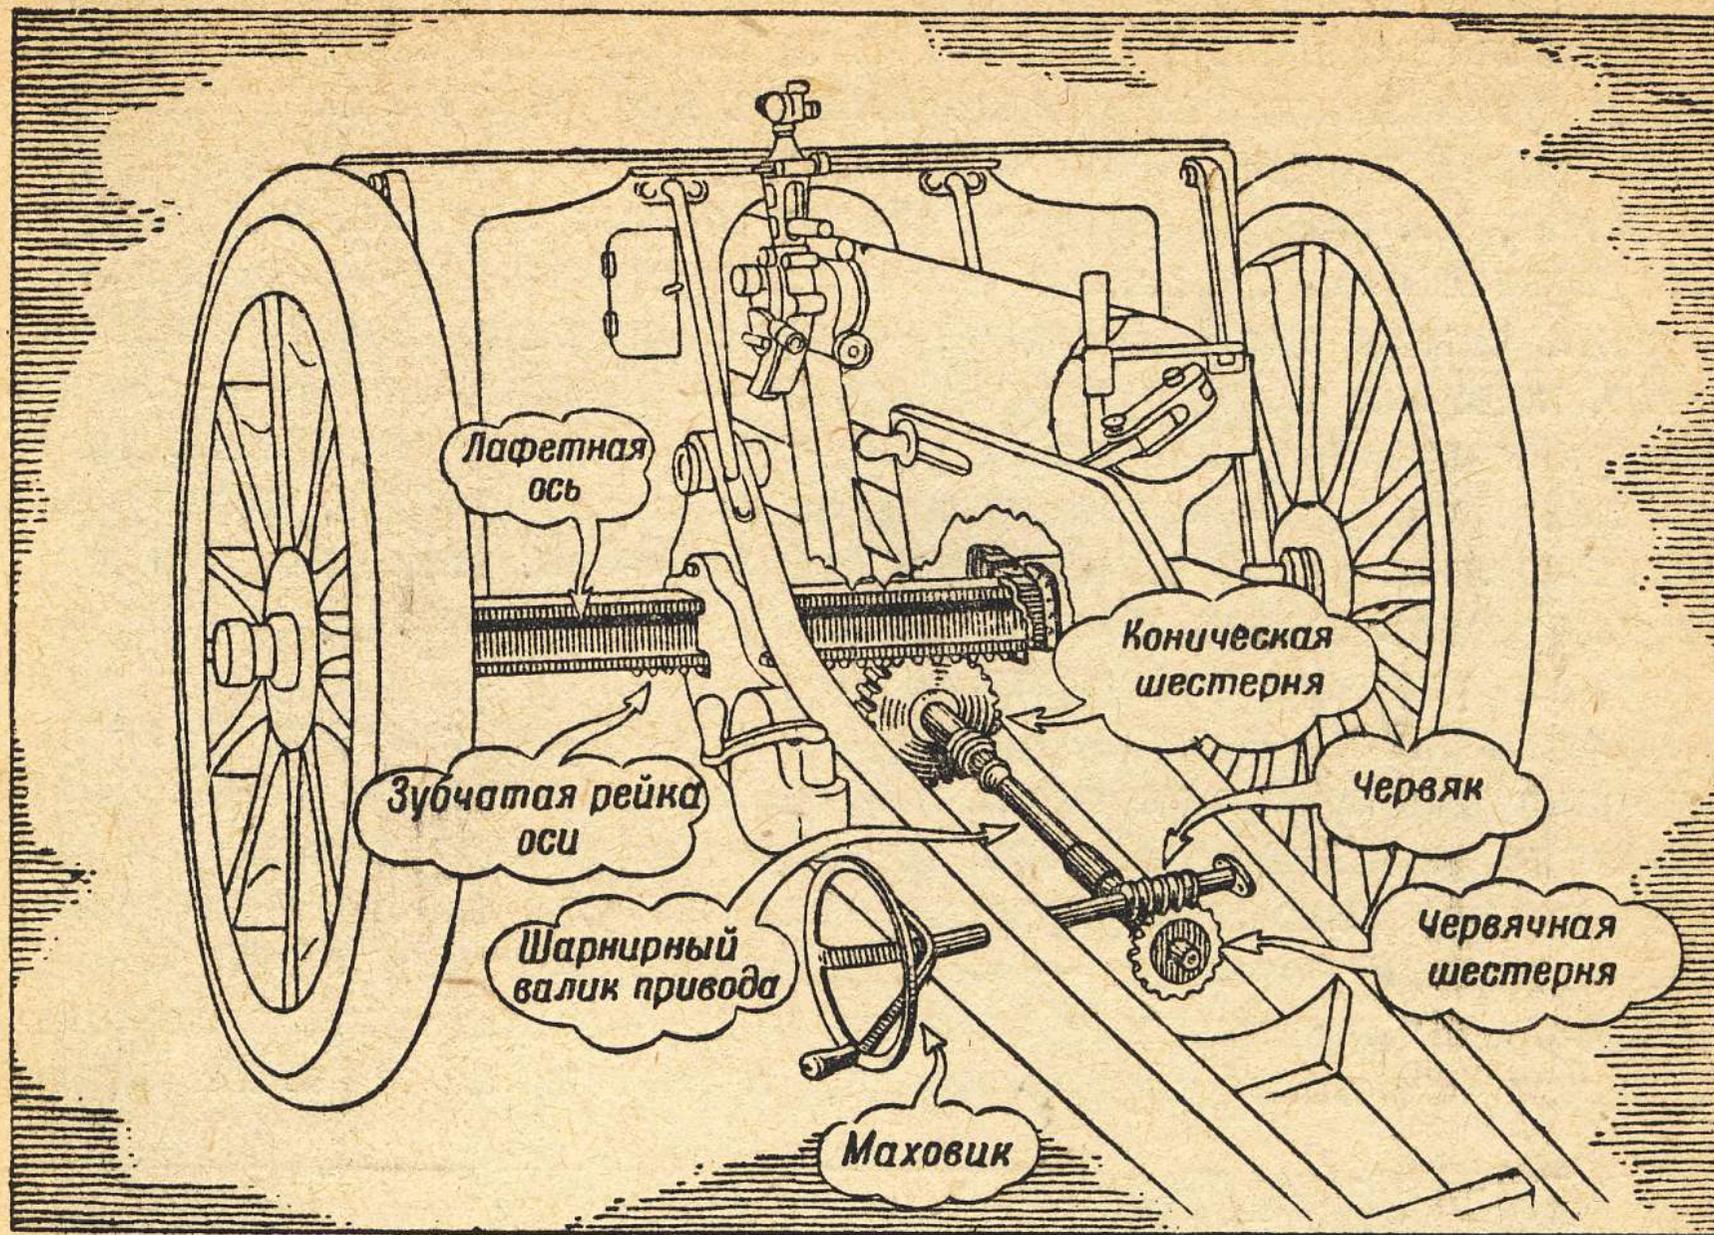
Как устроен поворотный механизм 76-миллиметровой полковой пушки (схема).
